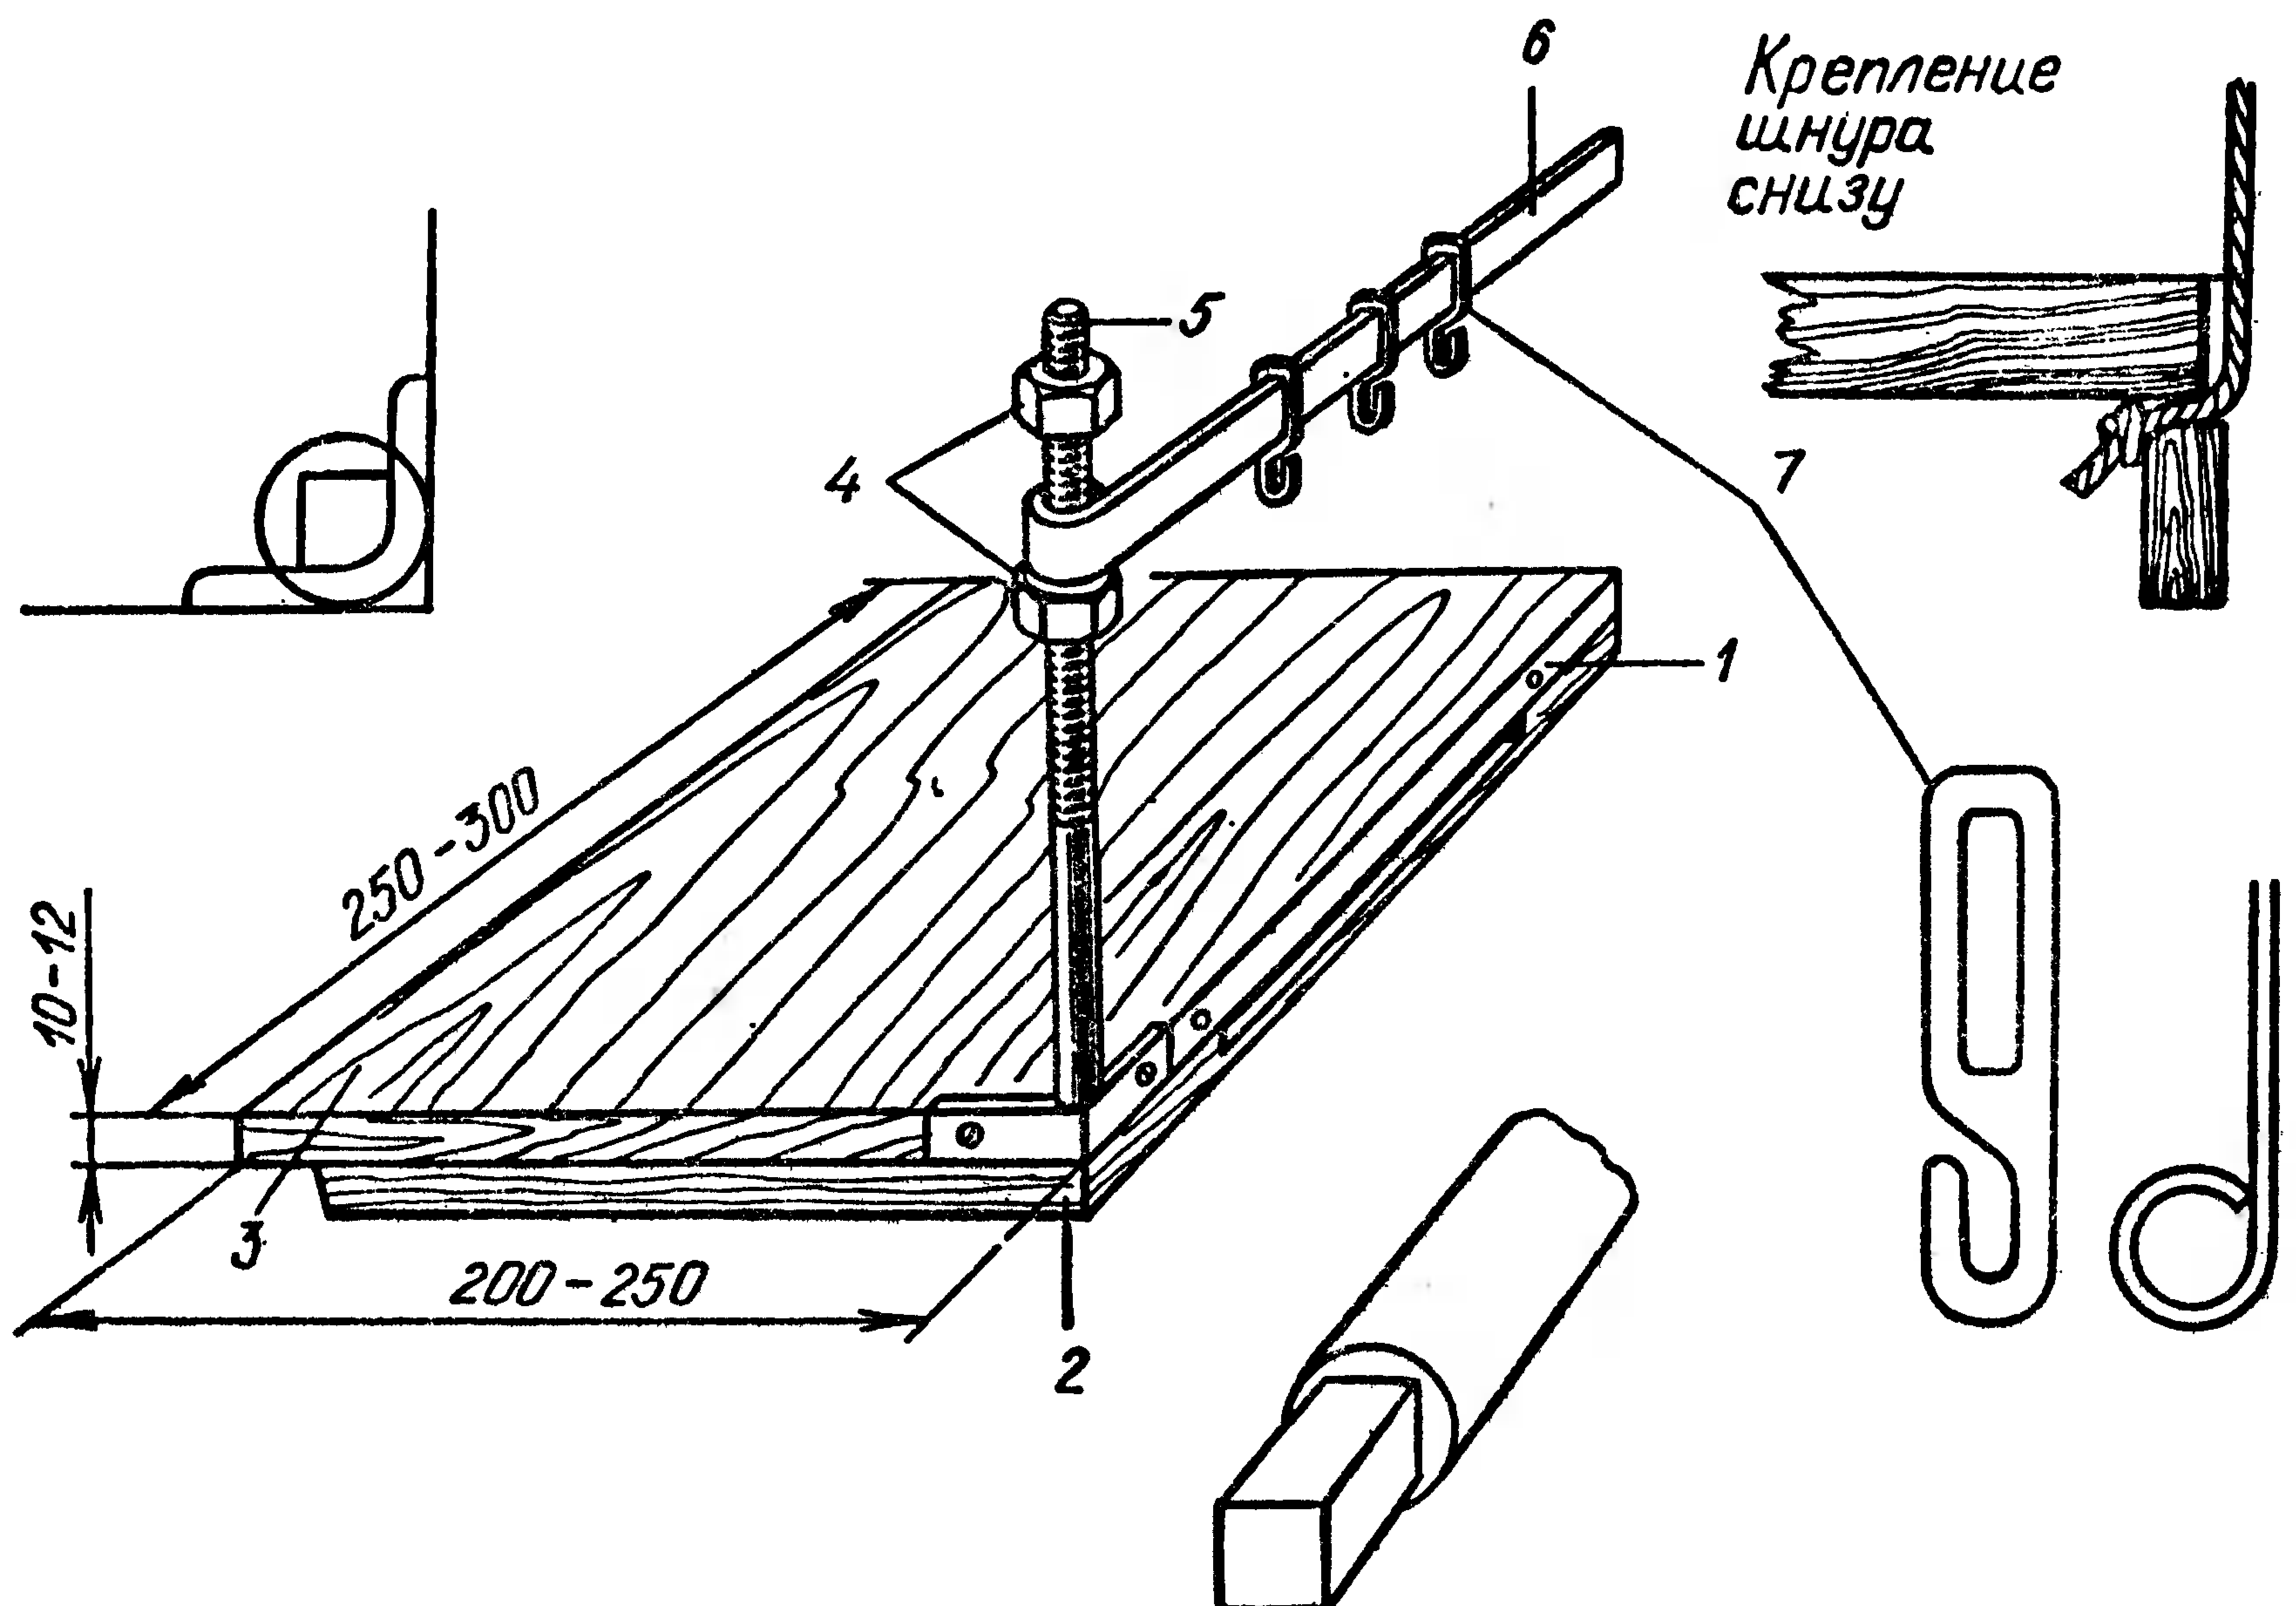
Сшивальный станок с одной стойкой: 1 — планка с прорезью; 2 — продольные ножки; 3 — основание; 4 — гайка; 5 — угловая стойка; 6 — пере- кладина; 7 — крючки.
